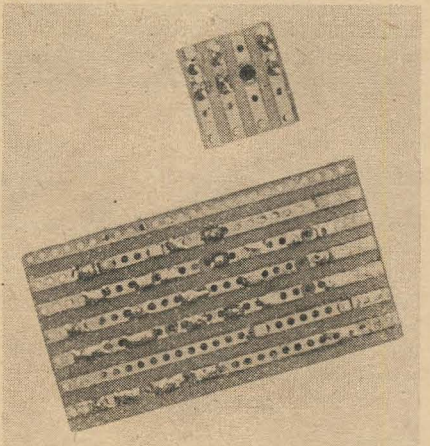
a) Bestückte Veroboard-Platte; b) Leiterseite
